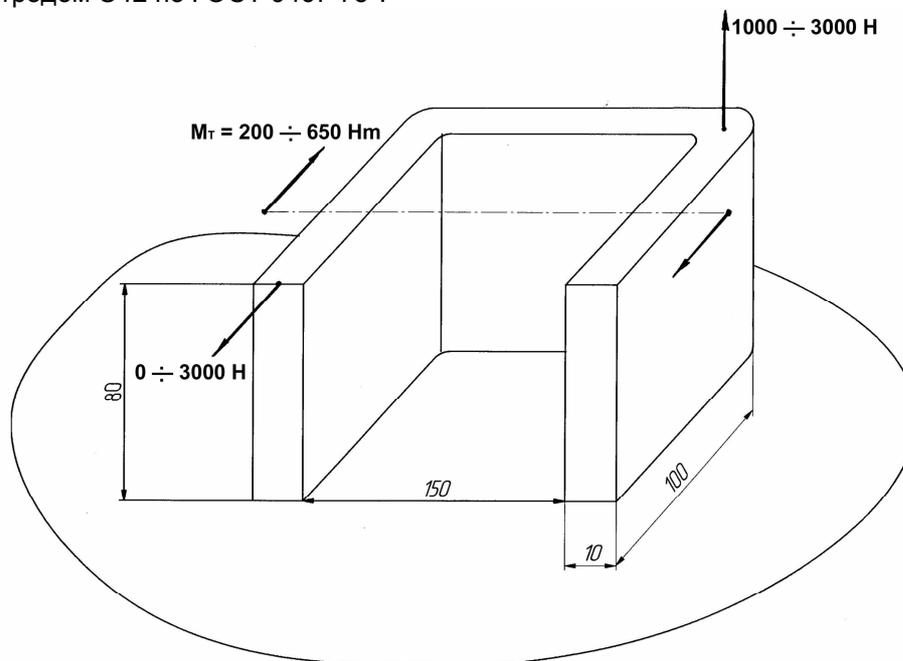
Расчетная модель таврового сварного соединения
